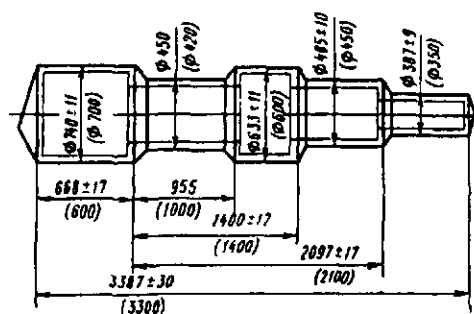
Примеры оформления разработанного чертежа поковки; цифры без скобок обозначают номинальный размер, цифры в скобках – размер детали
